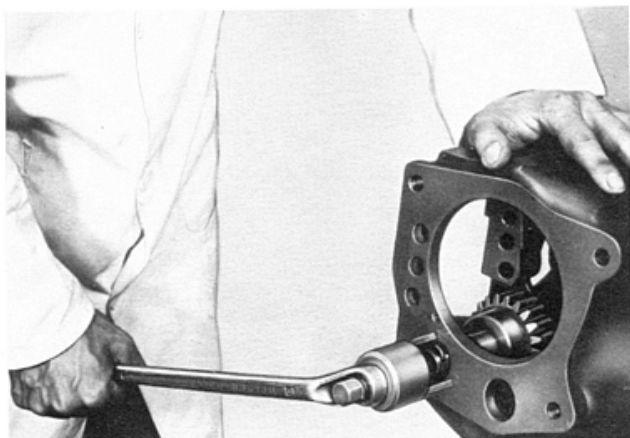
Remoção do eixo da engrenagem interm. marcha-a-ré
